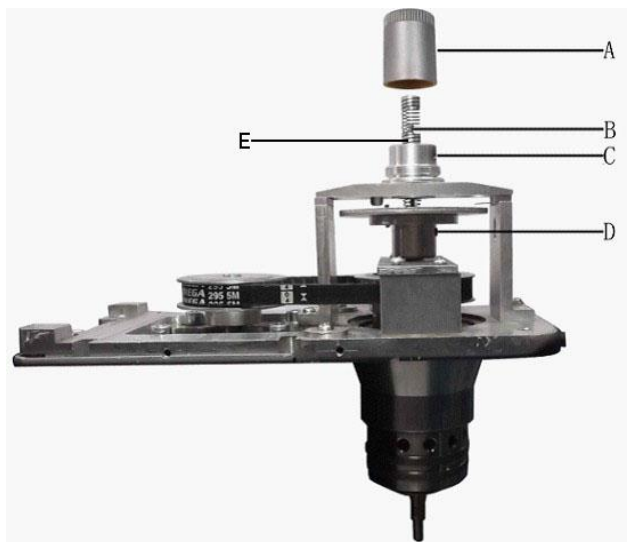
）外套筒的拆装 Diagram (III) Assembling and disassembling of outer sleeve
